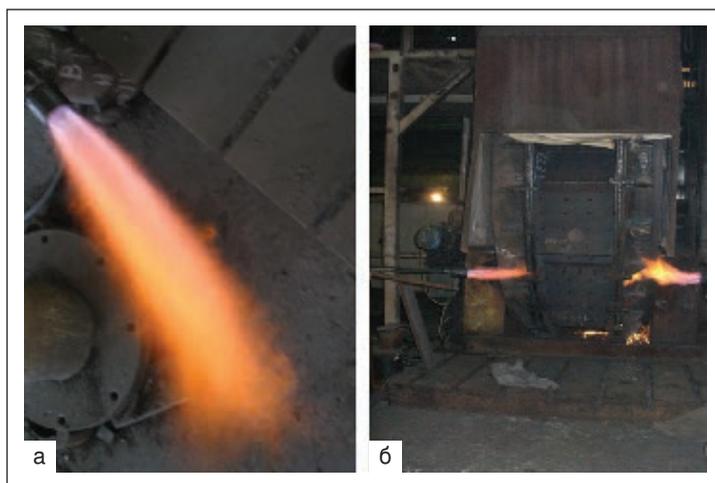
Горелка ГВ-М: а — факел длиной 800 мм; б — термическая правка сварного корпуса шириной 2,5 м и диаметром 6 м
